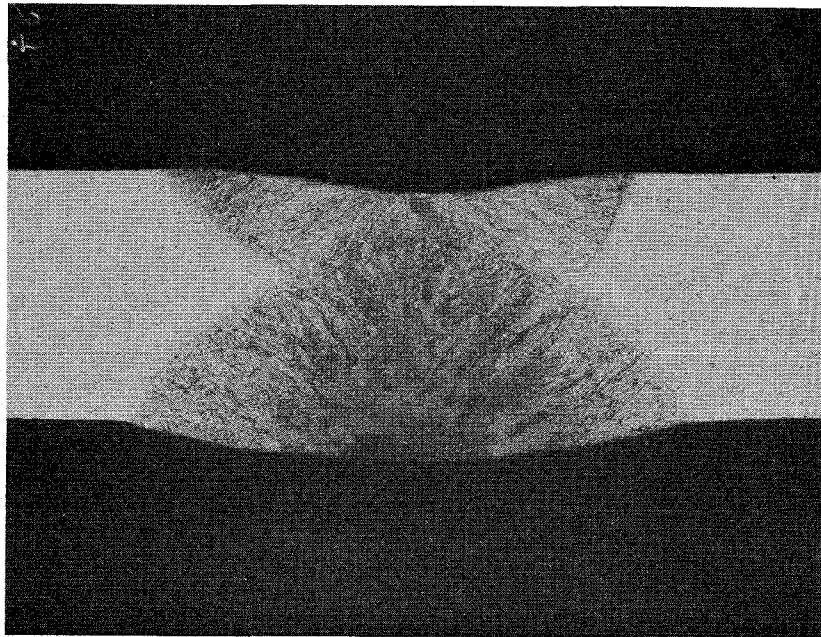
Makroaufnahme vom Querschliff der Schweißnaht bei Inconel 625 (Nr. 2.4856) im WS-Zustand nach vollständiger Entzunderung vor dem Schweißen (ungestörte Schweißnaht) $V = 10:1$
